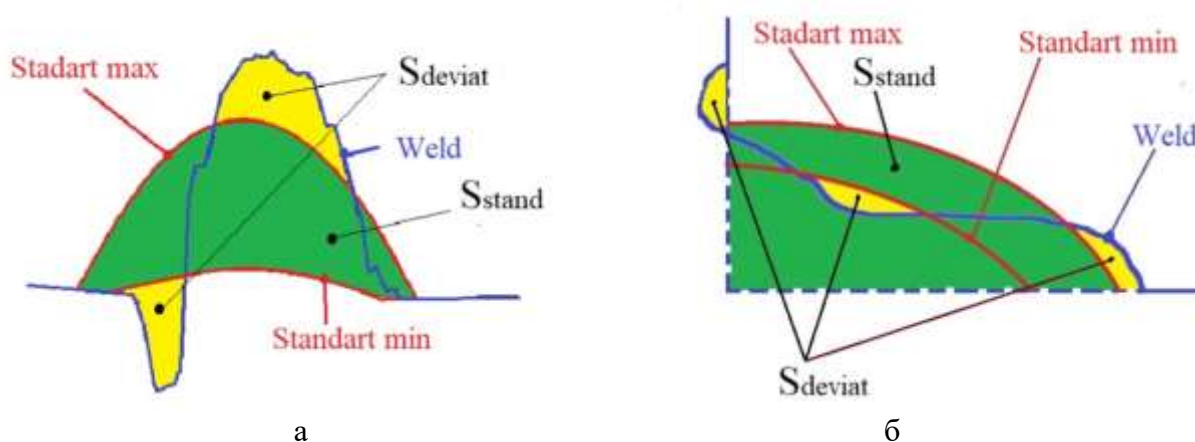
Схема сравнения цифровой реплики формы сварного шва с эталоном
